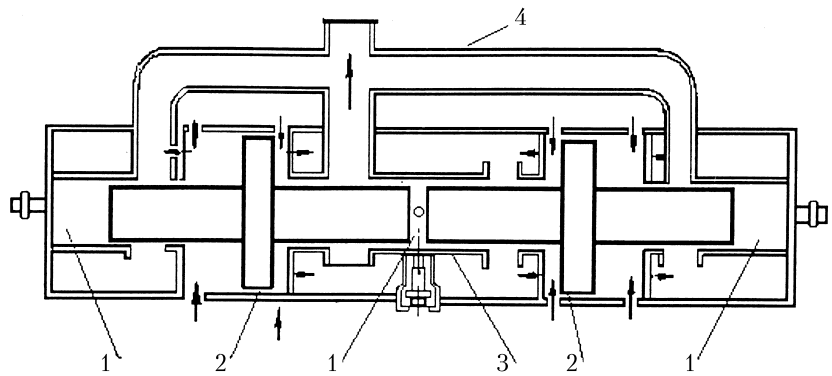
Свободнопоршневой генератор двустороннего действия: 1 — блок цилиндров; 2 — дизельный цилиндр; 3 — цилиндр компрессора; 4 — ресивер выхлопных газов
